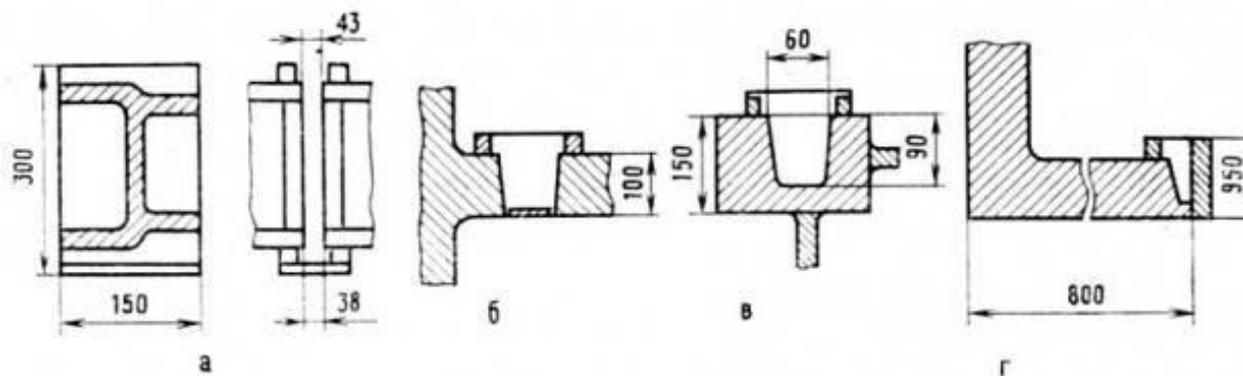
Примеры подготовки деталей к сварке:
